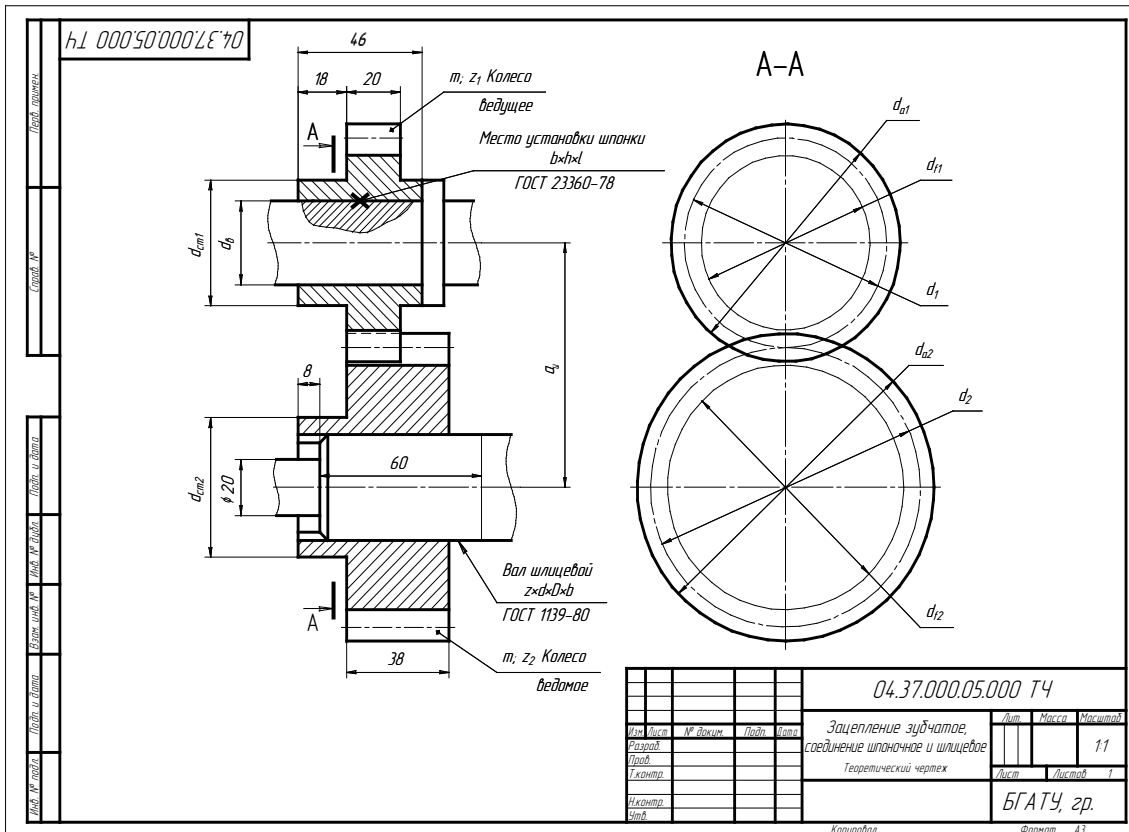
Исходные данные для выполнения чертежа зубчатой передачи
